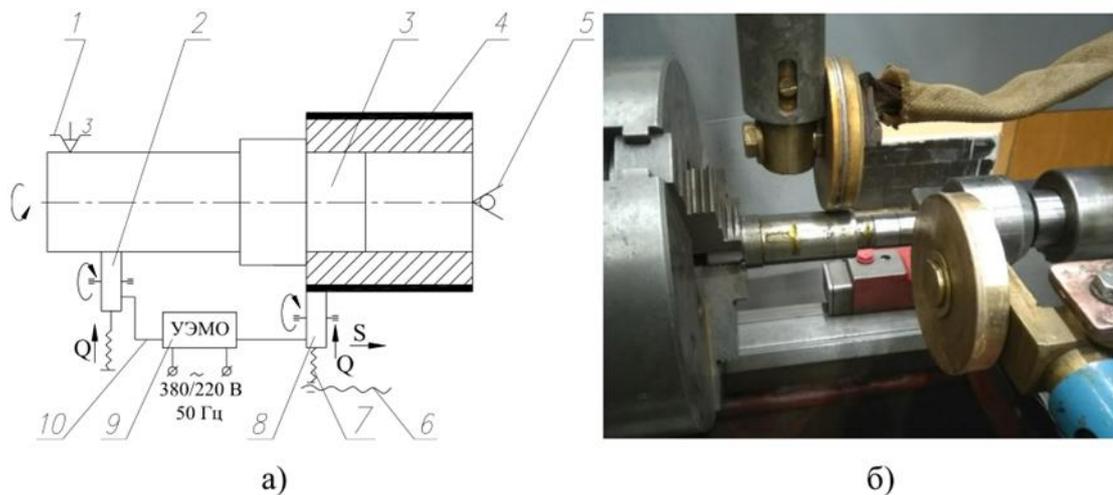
Схема ЕМПЗ: а) принципова схема; б) загальний вигляд. 1 – трикулачковий патрон, що самоцентрується; 2 – струмопідвідний ролик; 3 – оправлення; 4 – зразок; 5 – обертовий центр; 6 – ходовий гвинт верстата; 7 – телескопічна державка; 8 – інструментальний ролик; 9 – установка електромеханічного оброблення; 10 – струмопідвідні шини.
